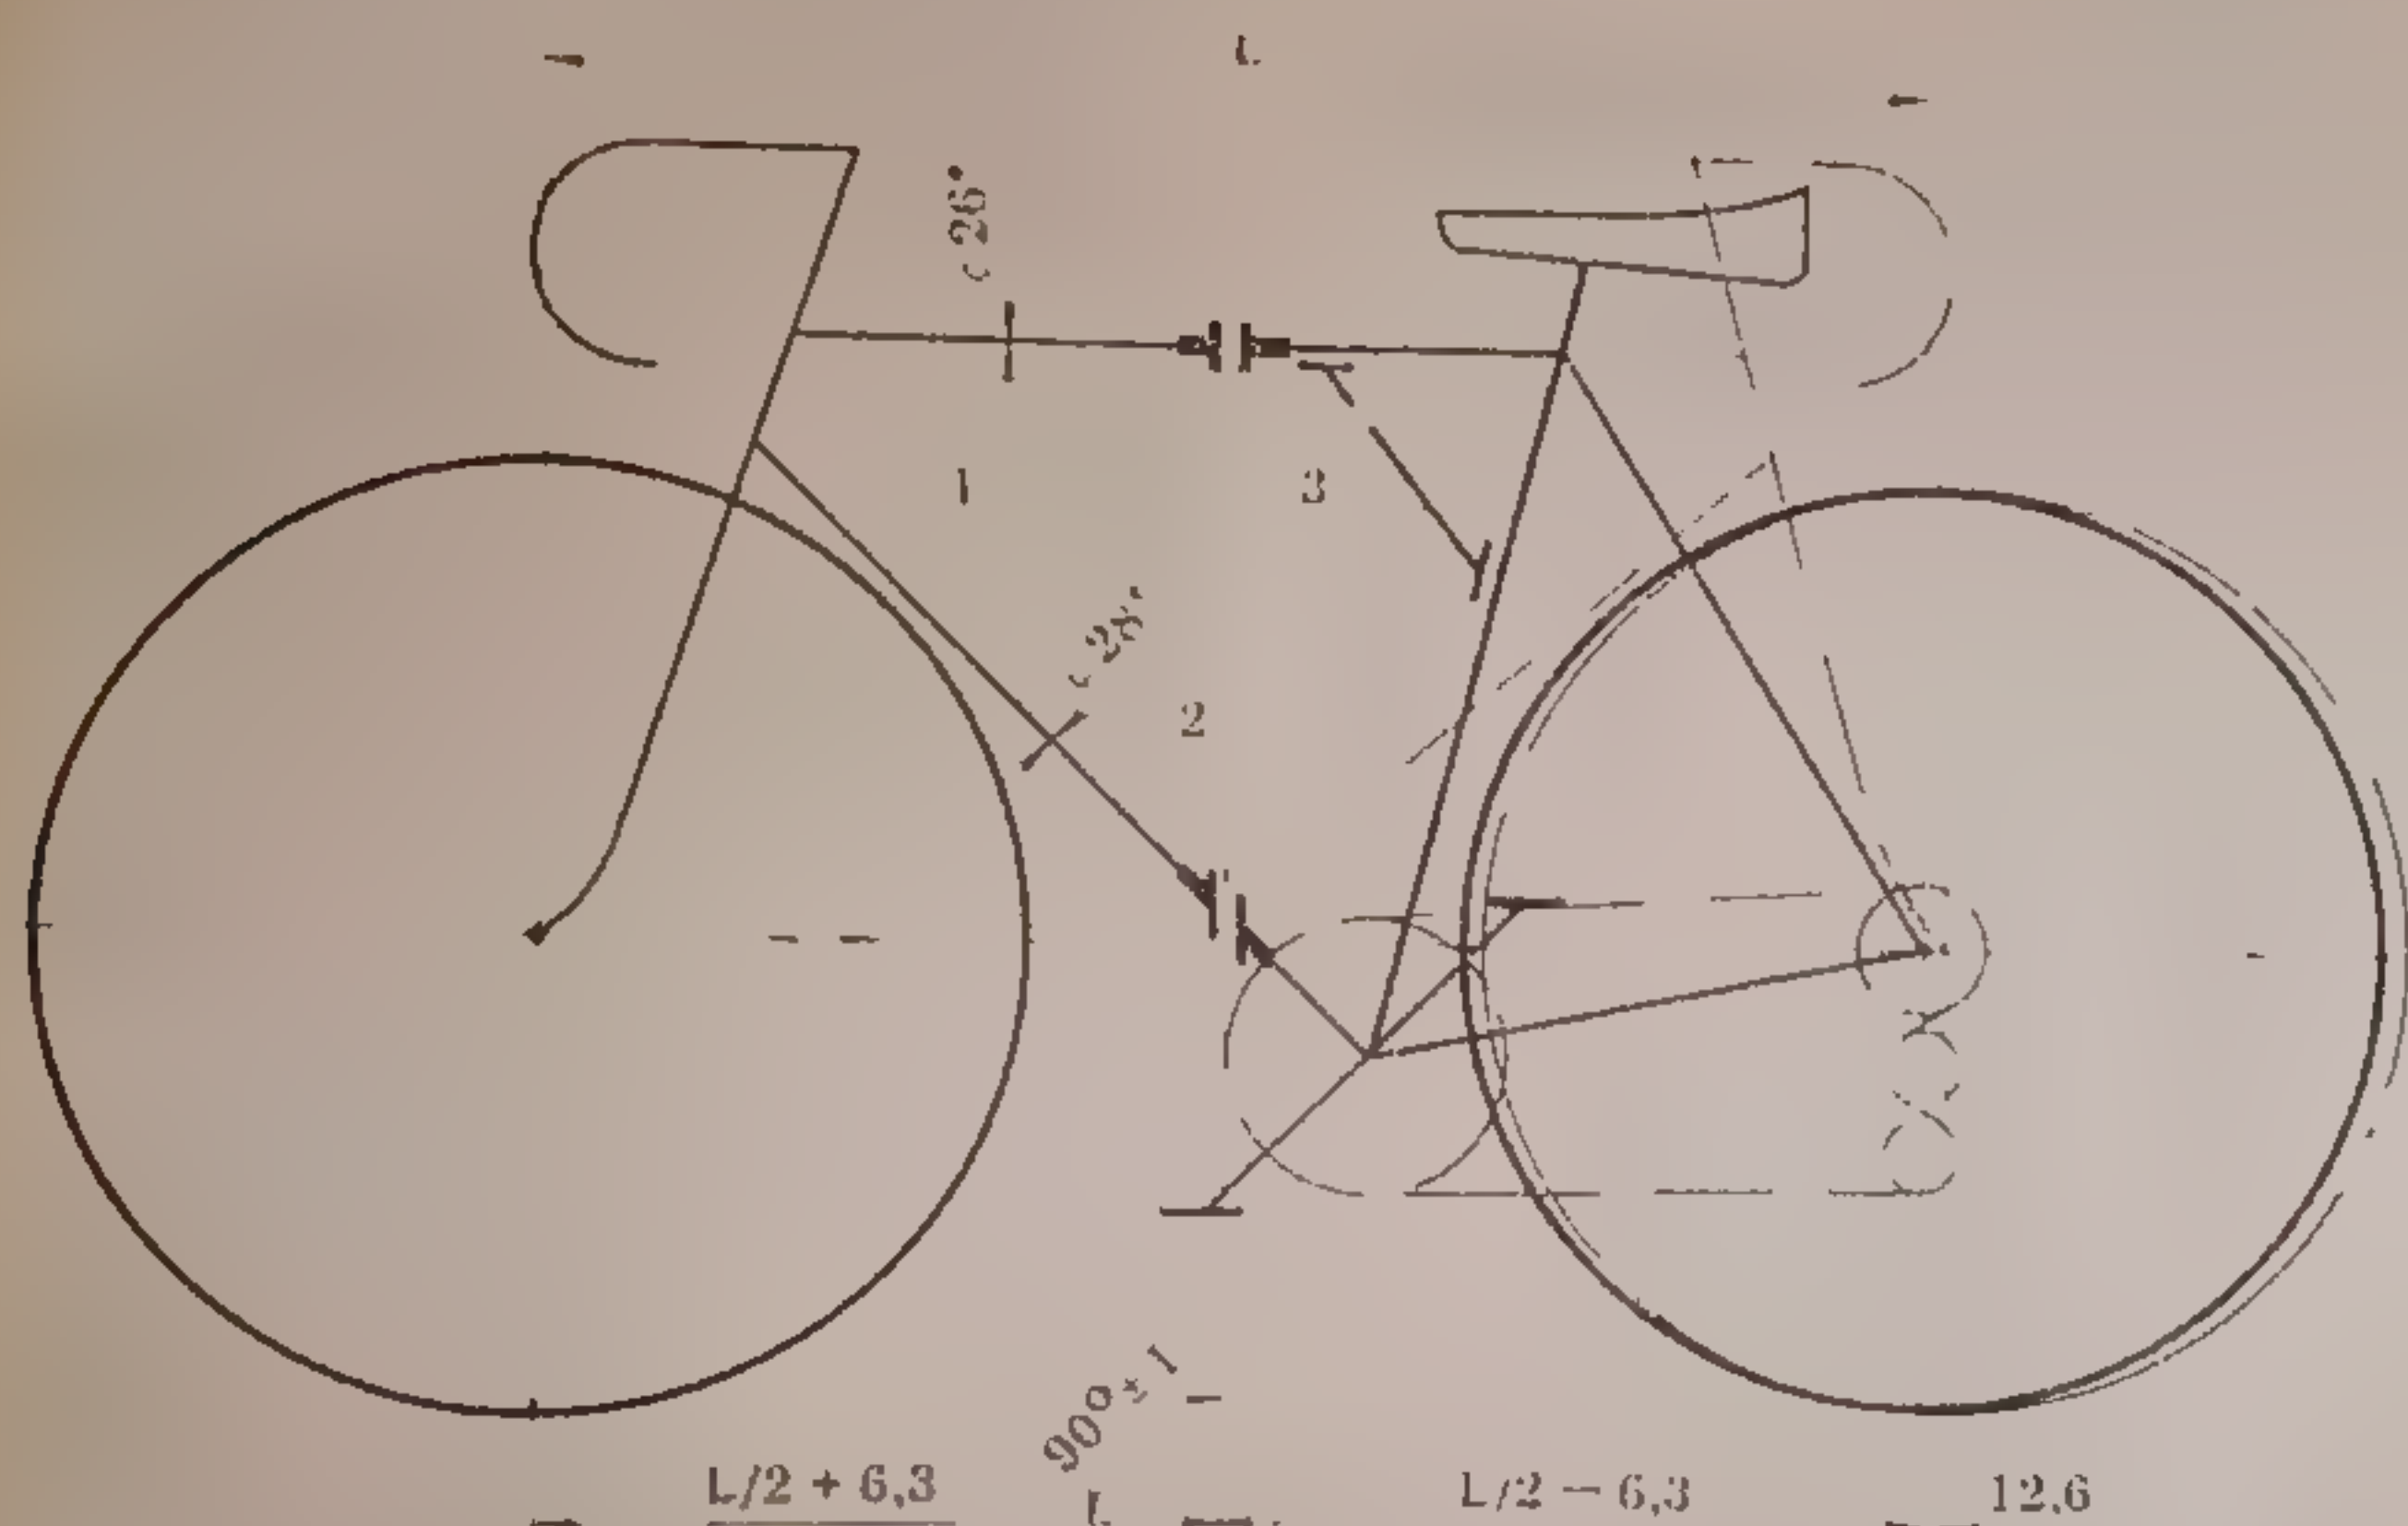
Разметка рамы под распил: 1 — верхний шарнир; 2 — нижний шарнир; 3 — распорка.
